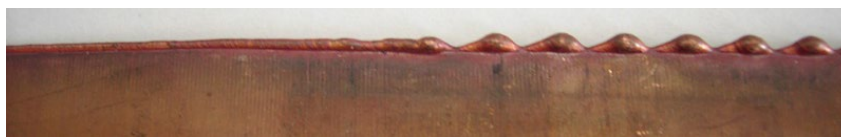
Основные режимы формирования сварных швов торцевых соединений (оплавление торца медной пластины толщиной 1,0 мм плазменной горелкой; скорость перемещения 2,8 см/с; слева – режим нормального формирования, ток дуги 80 А; справа – режим формирования структур типа Humping, ток дуги 100 А; шаг периодичности структур – 7 мм)
